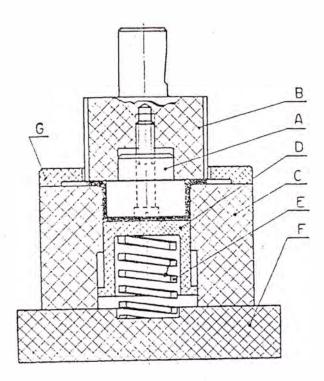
Esquema de una estampa sencilla para embutir.
